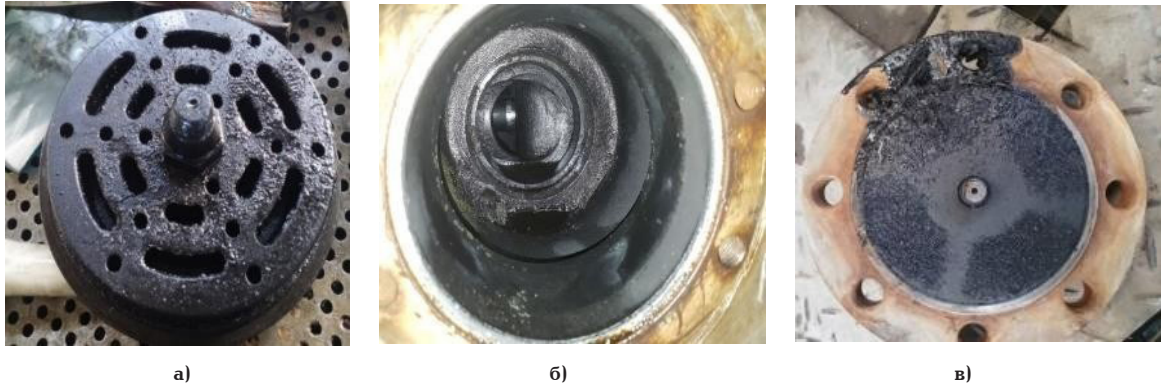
Образование загрязнений на второй ступени подпиточного компрессора:
